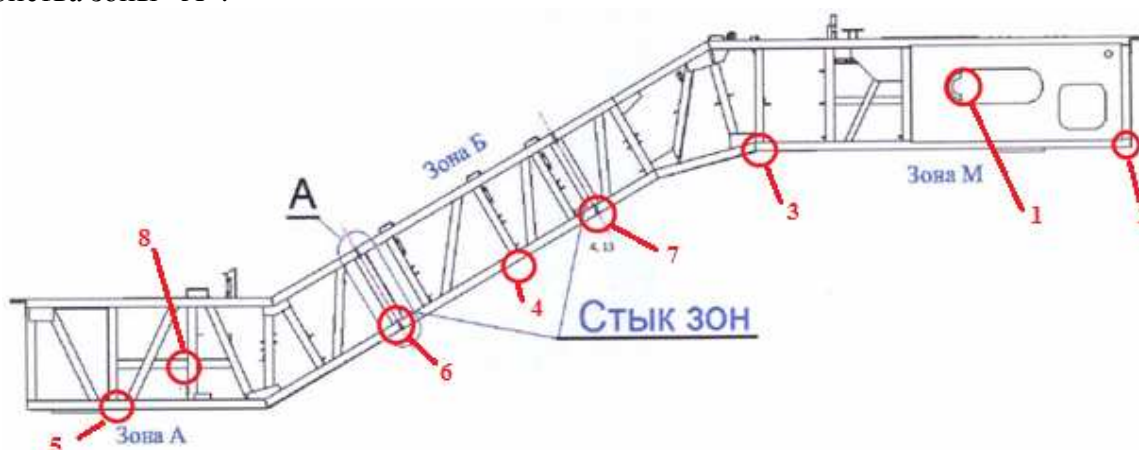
Места измерения пространственного вектора виброускорения: 1 – вертикальные листы зоны М; 2, 4, 5 – места установки опор; 3 – зоны крепления криволинейных направляющих; 6, 7 – зоны стыков; 8 – элементы направляющих натяжного устройства
